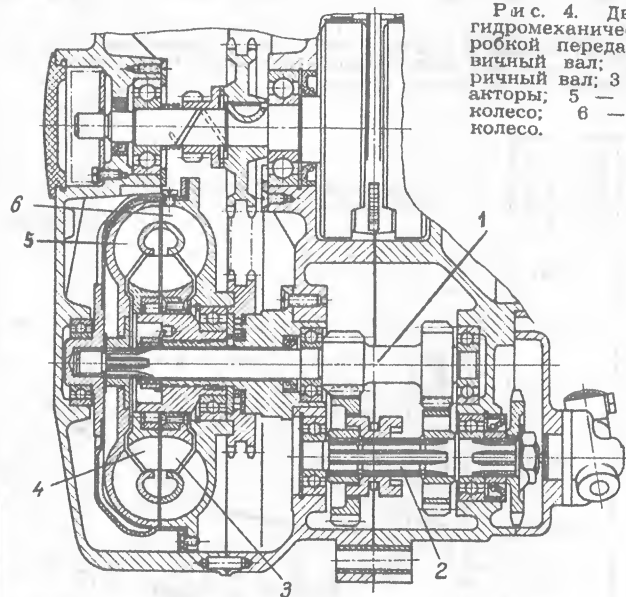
Двигатель с гидромеханической коробкой передач: 1 — первичный вал; 2 — вторичный вал; 3 и 4 — реакторы; 5 — турбинное колесо; 6 — насосное колесо.
